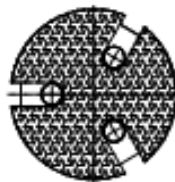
Фрезер забойный типа ФЗ тяжелого вида
